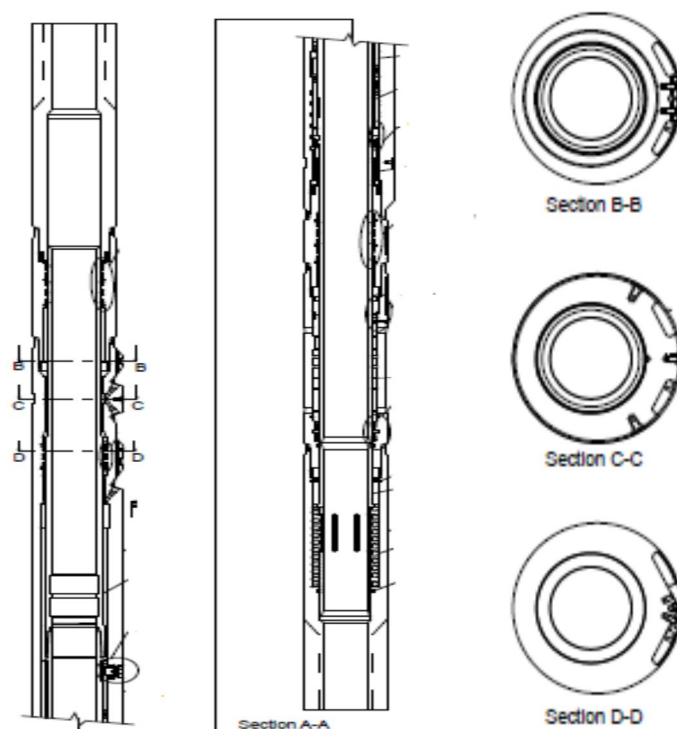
Чертеж общего вида многопозиционного клапана контроля внутритрубного притока ODIN-LP [4]
